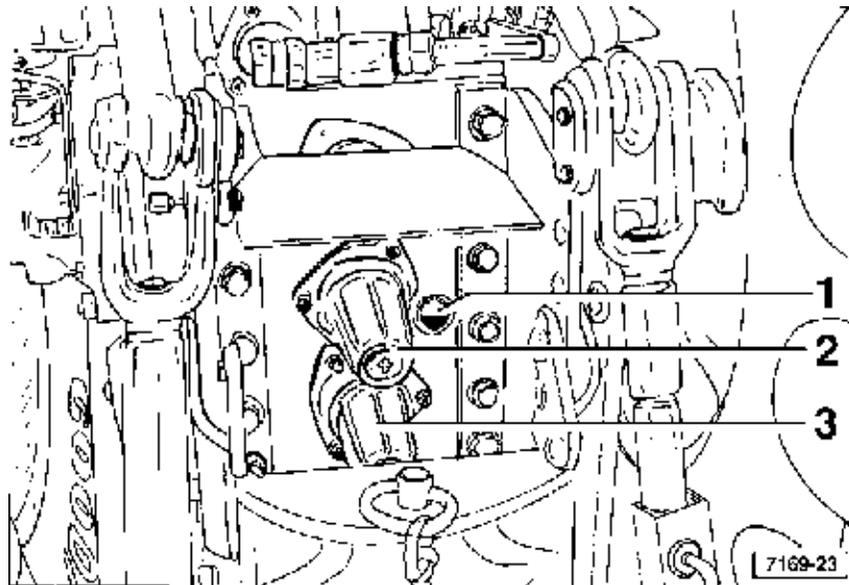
Bout d'arbre de la P.D.F. arrière
